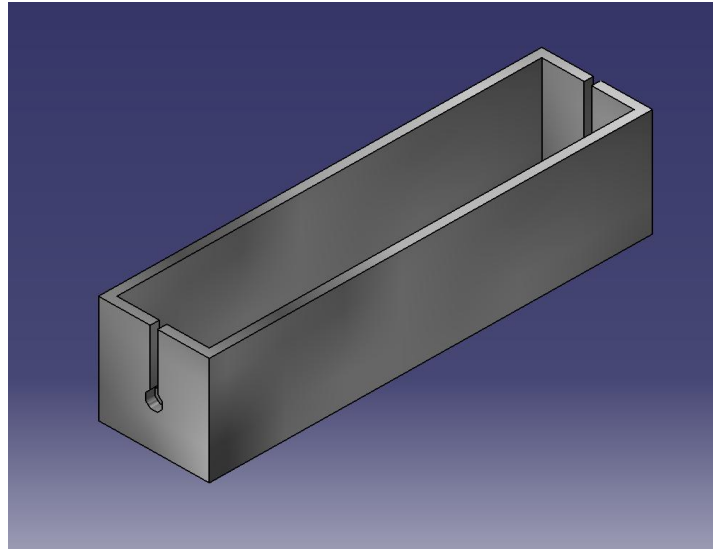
CAIXA DE MOLDE – 20 CM DE COMPRIMENTO
